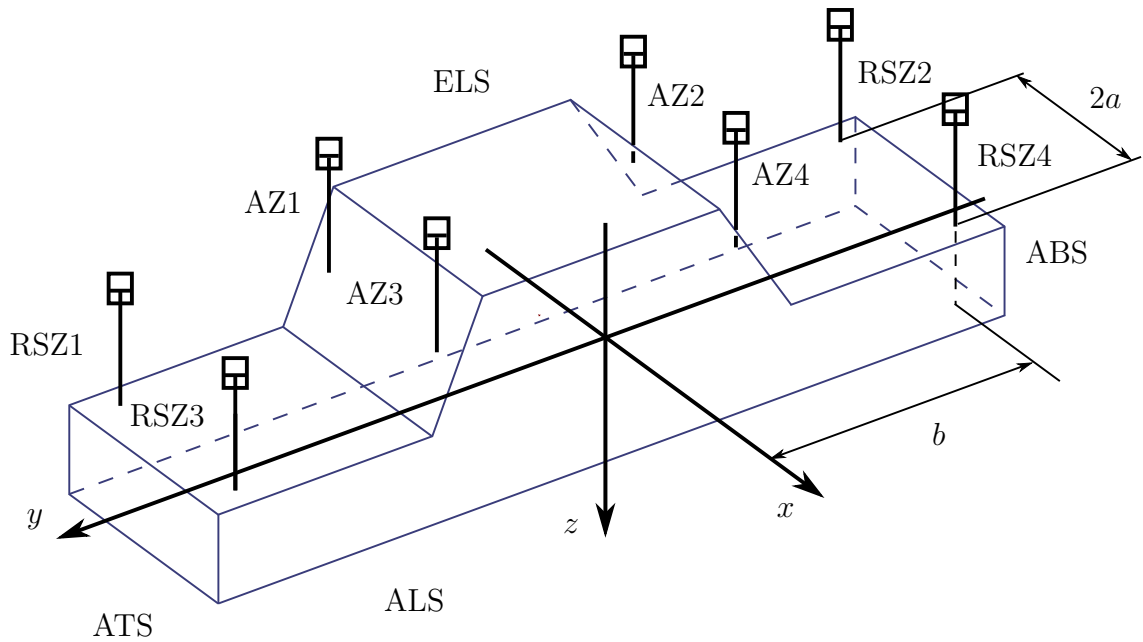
Skizze des Druckrahmens einer Richtmaschine
